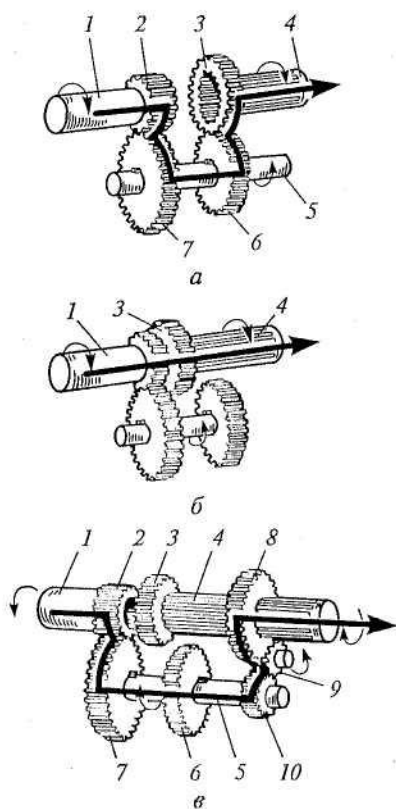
Схема работы трехвальной коробки передач: а, б — движение вперед; в — движение задним ходом; 1 — первичный вал; 2, 3, 6, 7, 8, 9, 10 — шестерни; 4 — вторичный вал; 5 — промежуточный вал
